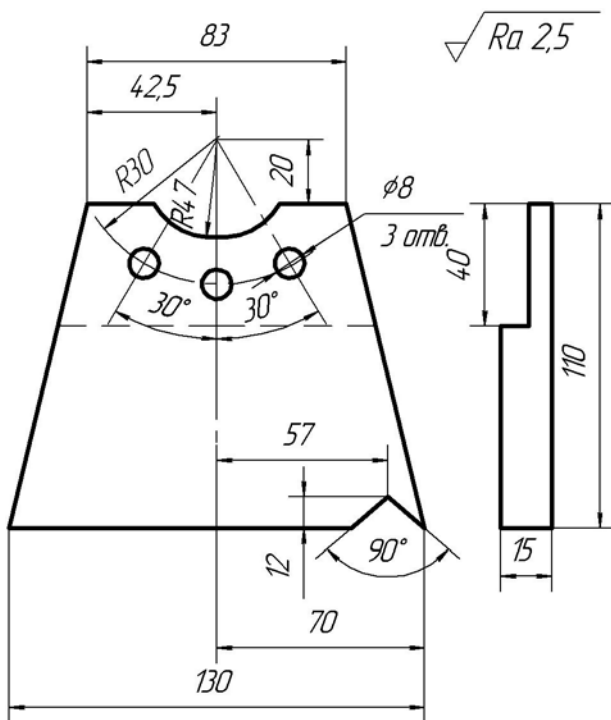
Кресленик деталі з однаковою шорсткістю всіх поверхонь
